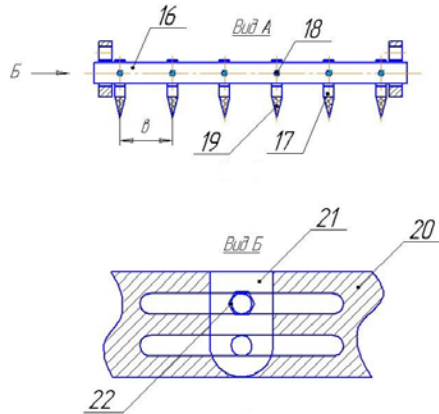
Разравниватель в сборе с механизмом крепления
